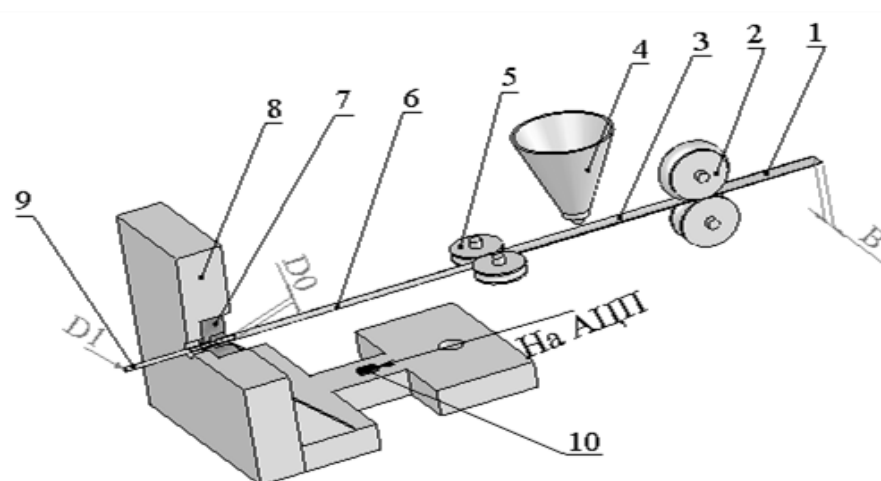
Експериментальна установка для волочіння порошкового дроту: 1 – металева стрічка; 2 - профілезгинаюче обладнання; 3 – сформований жолоб; 4 – автоматичний дозатор; 5 – ролики, що калібрують; 6 – заготовка порошкового дроту; 7 – філь’ера ; 8 – волокоутримувач; 9 – порошок дріт; 10 – система тензодатчиків.
